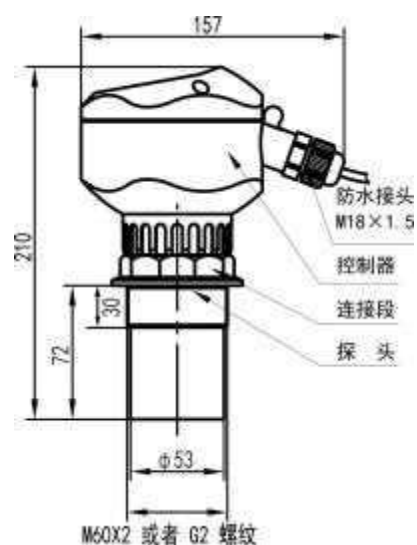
M60×2 或者 G2 螺纹传感器结构尺寸
